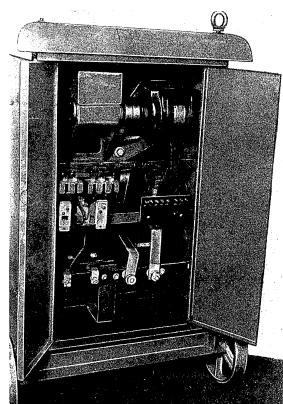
Сварочный трансформатор ТСД-500
